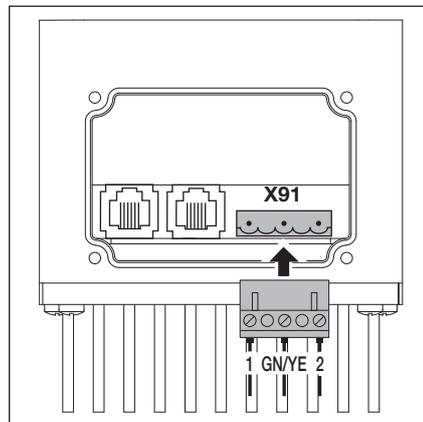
Anschluss der Motorleitung an die Motoranschlussplatine
